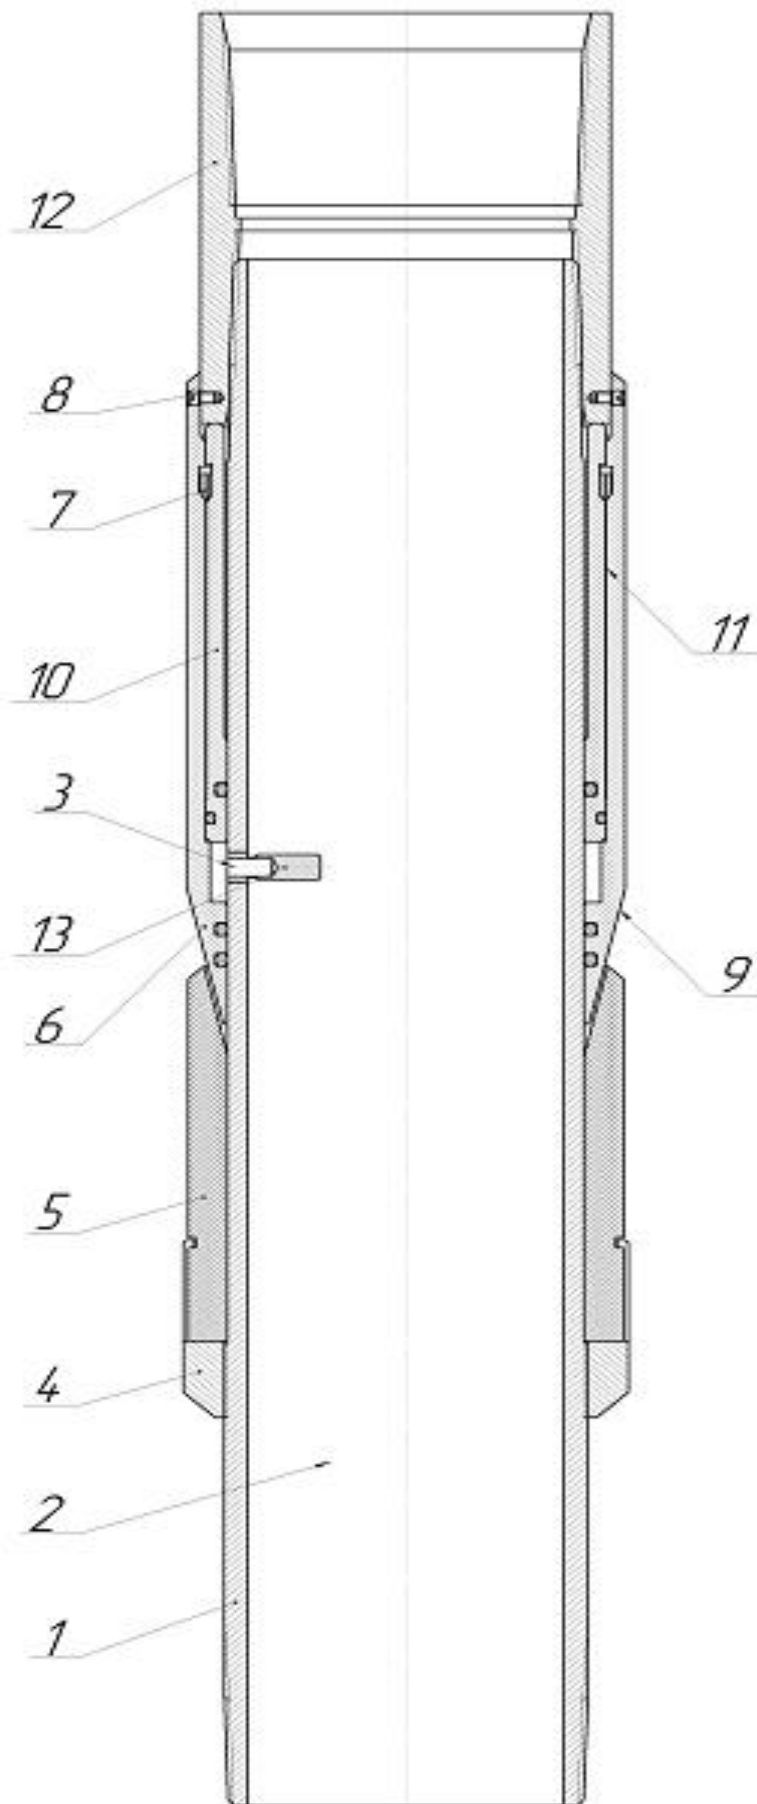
Пакер закоронный гидравлический ПЗГ-102Г (ПЗГ-102ХОС)
